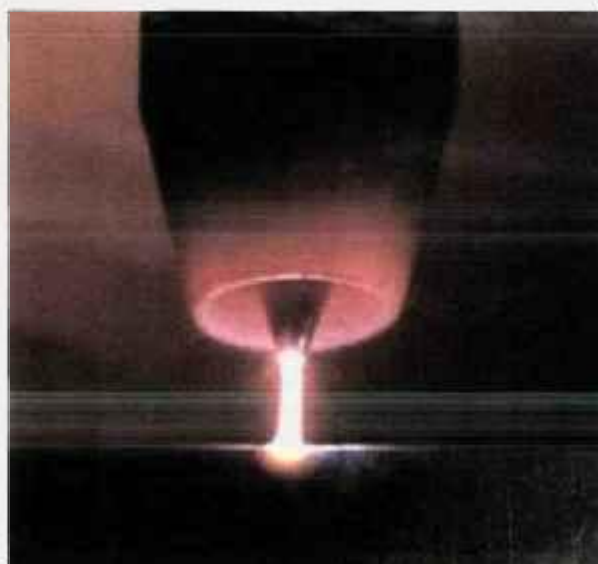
Soldagem – feixe de plasma⁸⁵.
